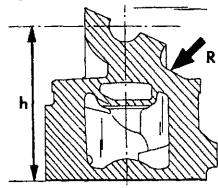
Расположение маркировки "R" на головке цилиндров, обработанной под повышенный размер. Высота головки цилиндров измеряется между стрелками "h".
